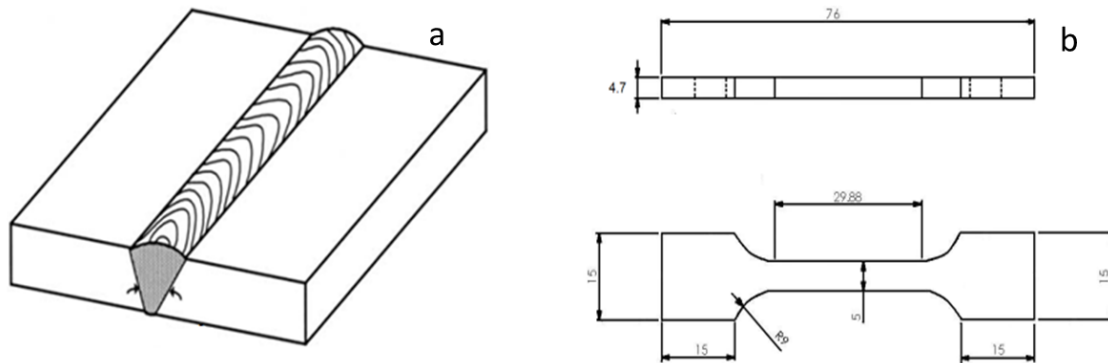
Representación esquemática de la unión soldada y el espécimen usado en las pruebas cuasi-estáticas (dimensiones en mm)
